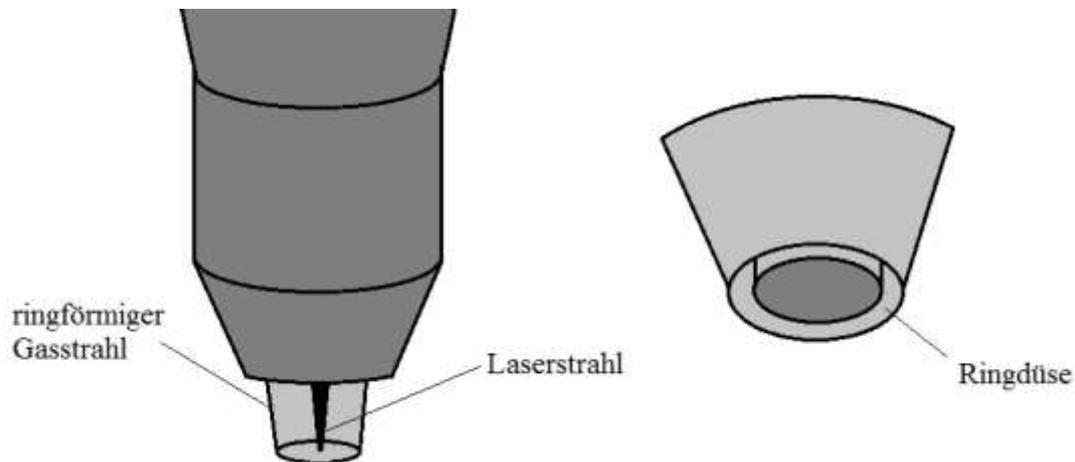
Aufbau einer Ringdüse als pneumatischer Abstandssensor
